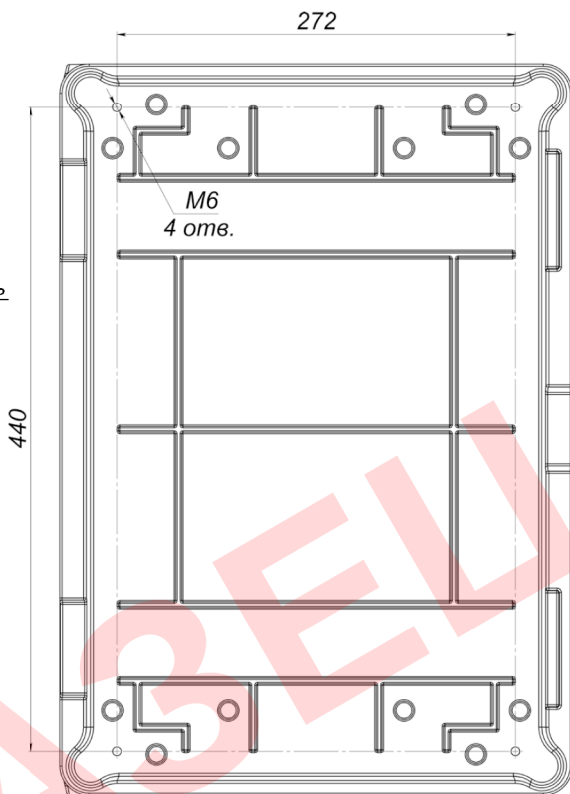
Расположение и габариты отверстий для крепления к стене
